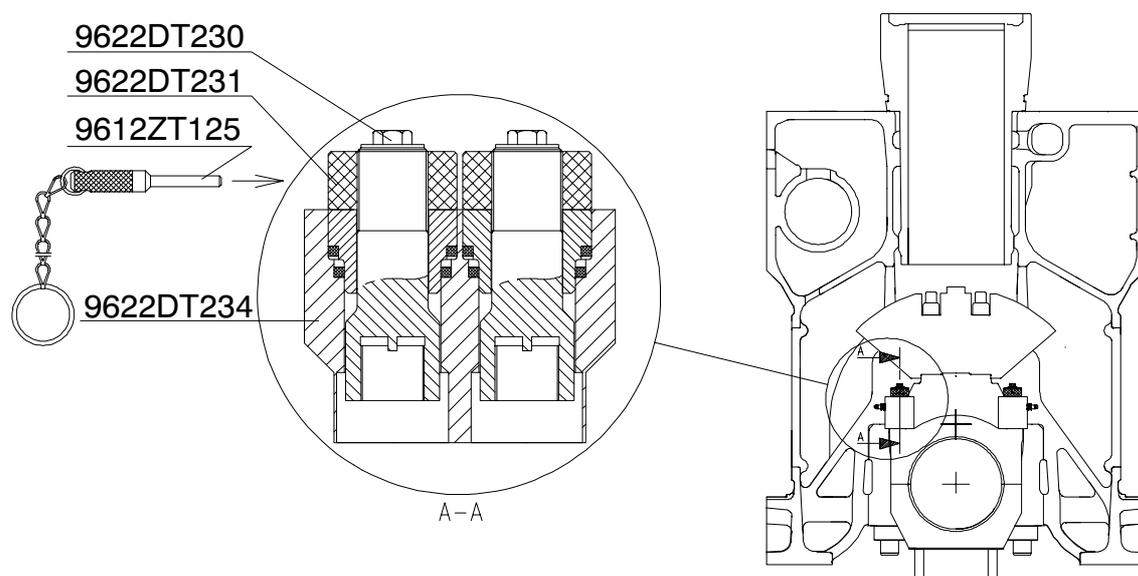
19 Herramienta hidráulica, espárragos de cojinete de cabeza de biela
